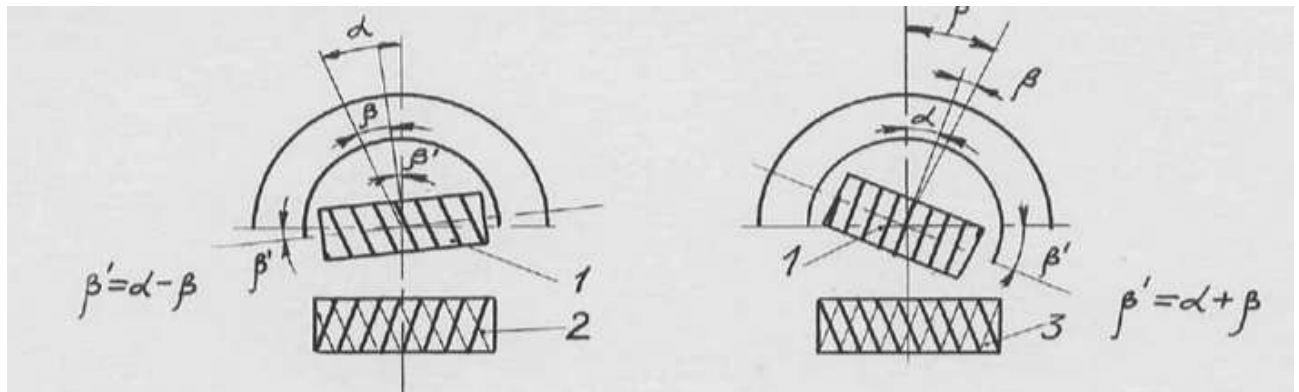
Схема установки червячної фрези при нарізанні зубчастих коліс [4]
